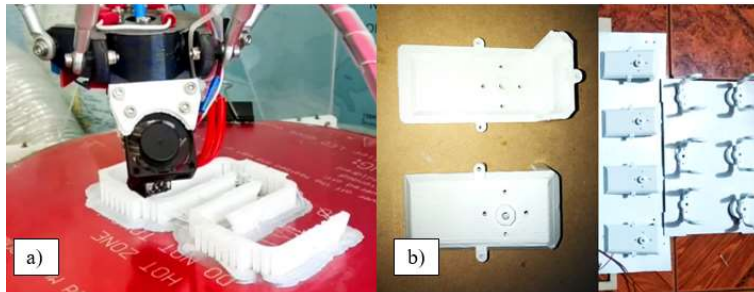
Manufactura de la estructura: a) impresión FDM, b) acabados
